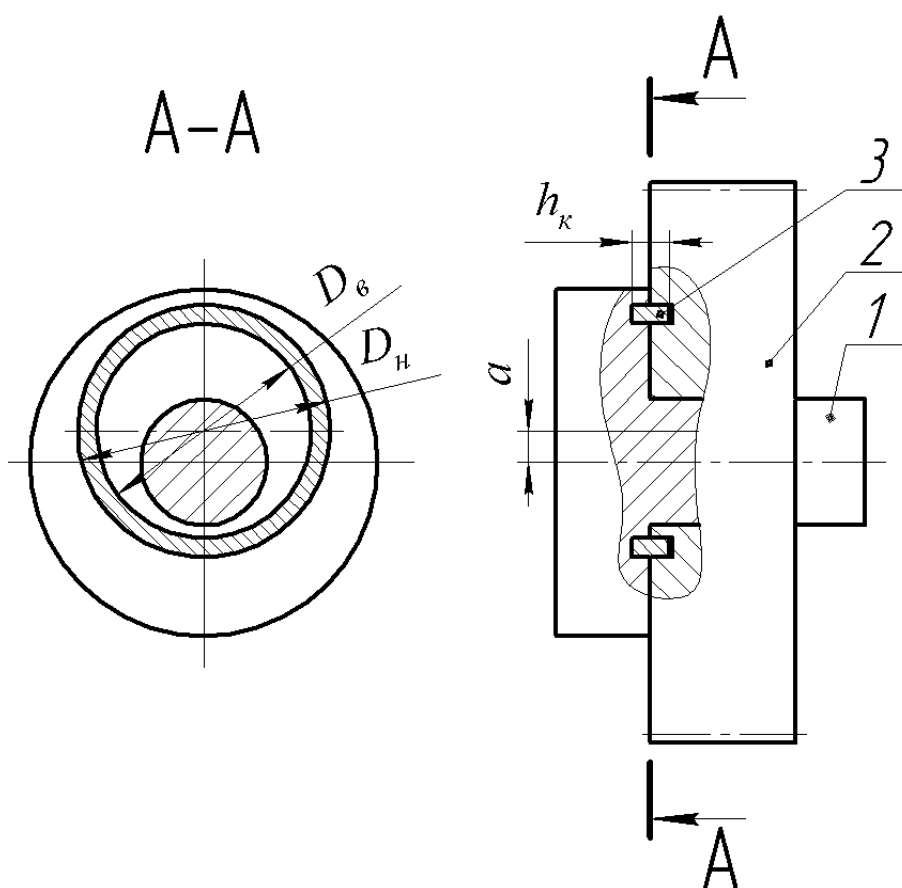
Соединение вала и ступицы с помощью втулки: 1 – вал; 2 – колесо; 3 – шпонка
